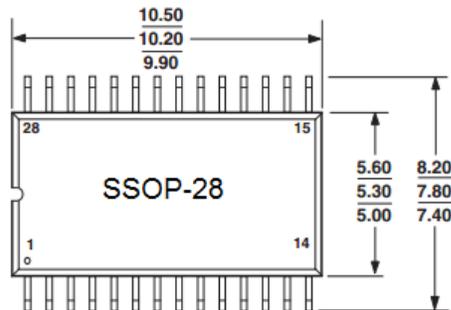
Dimensiones del CI AD9850 en milímetros.
